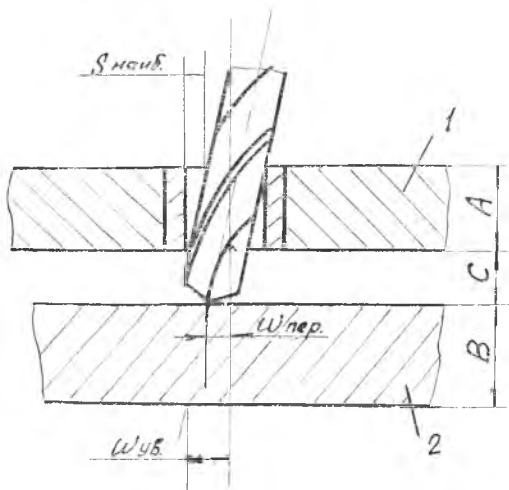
Схема определения погрешности увода оси сверла: 1 — кондуктор; 2 — заготовка
